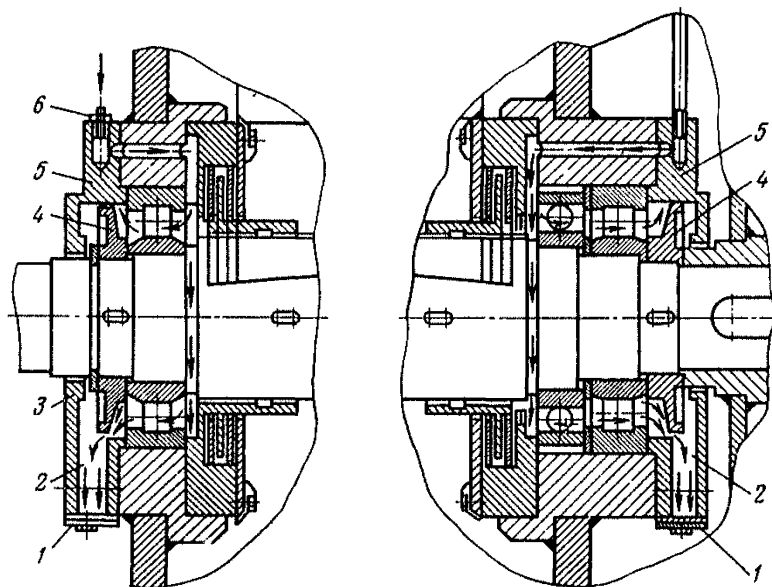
Подшипниковые узлы двигателей ВАО:
